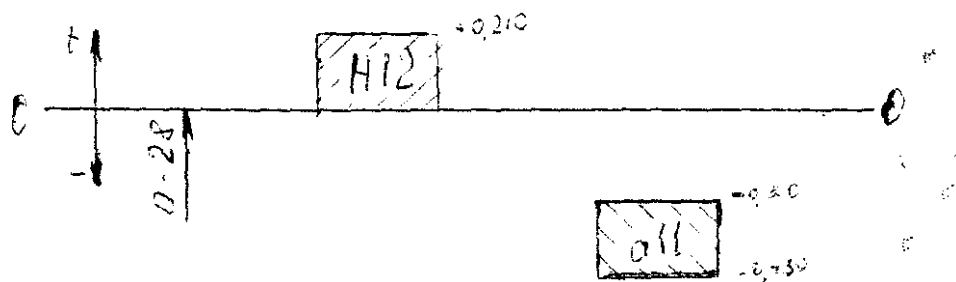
Схема розміщення полів допусків для розміру D
